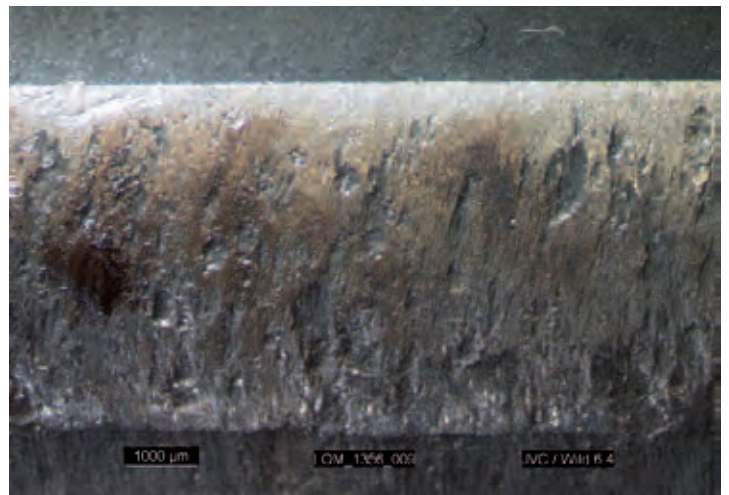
Zahnflanke, teilweise mit flächigen Ausbrüchen durch Zerrüttung
